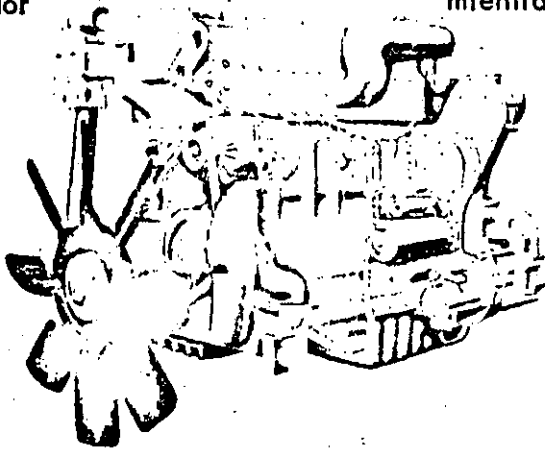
Motor Caterpillar de Diesel D343 (988)
